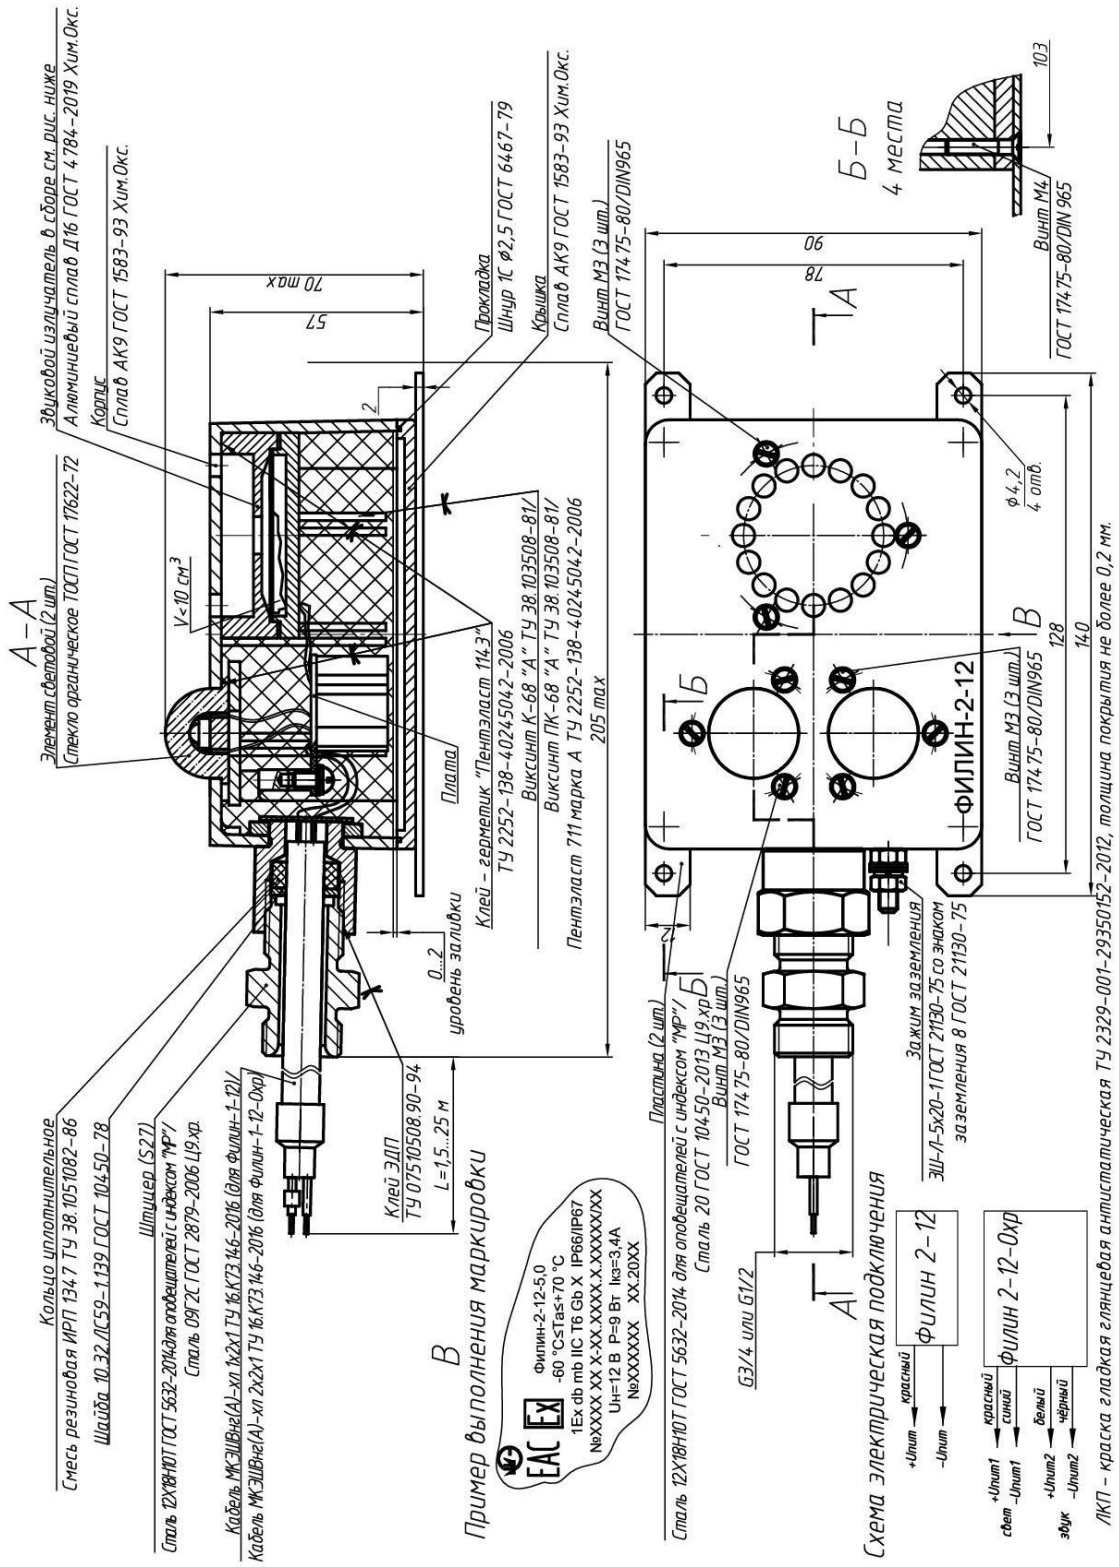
а – Габаритный чертёж оплещателей ФИЛИН-2-12 и ФИЛИН-2-12-Охр (без вилок), совмещённый с чертёжом средств взрывозащиты
